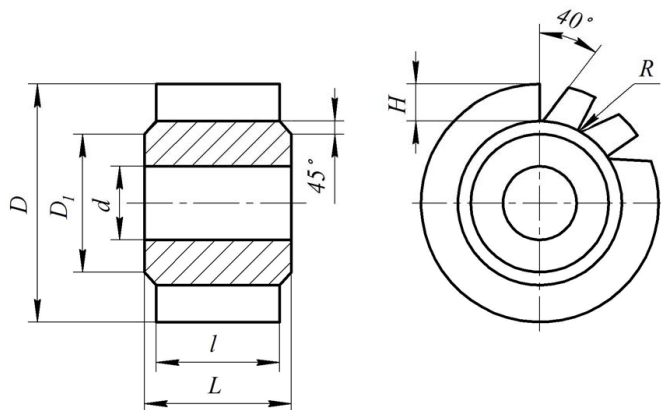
Конструкция заготовки червячной фрезы из твердого сплава
